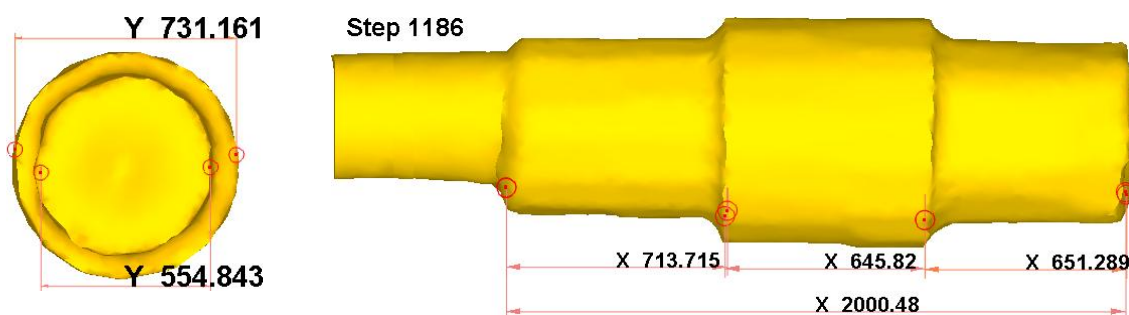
Размеры поковки после промежуточной протяжки
